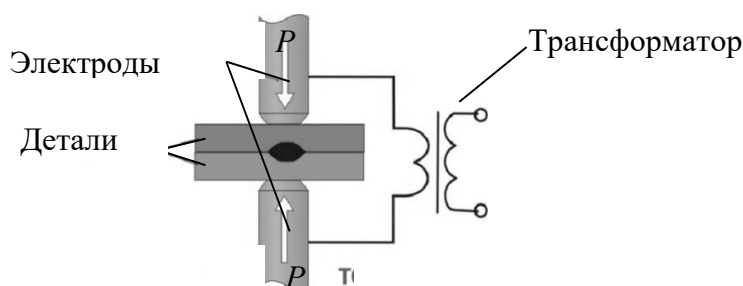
Схема точечной сварки давлением
